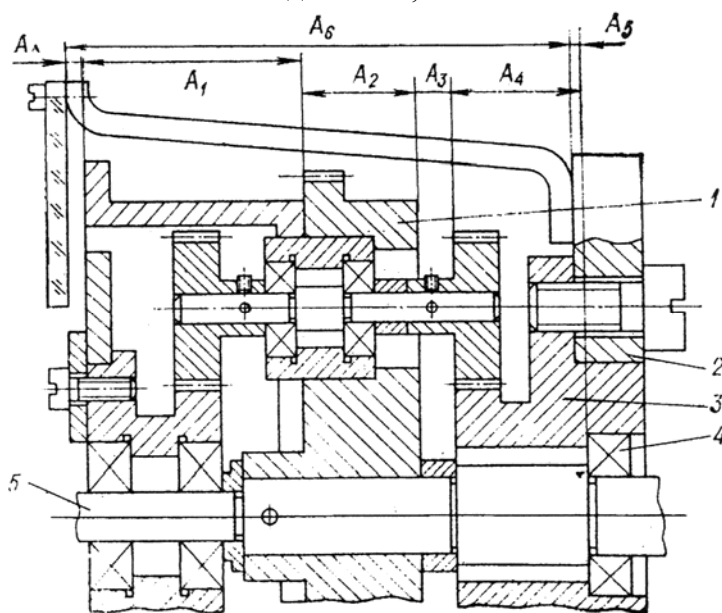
Узел подшипникового соединения: 1 – водило; 2 – плита; 3- колесо;
